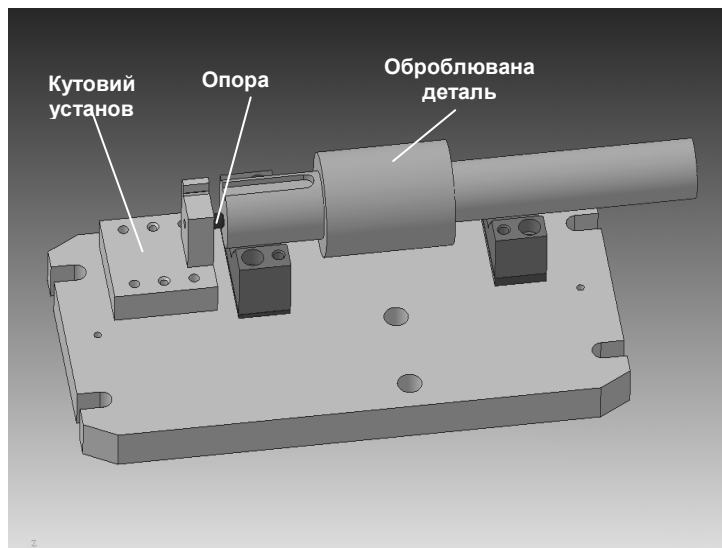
Встановлення деталей для запобігання повздовжнього зсуву вала
